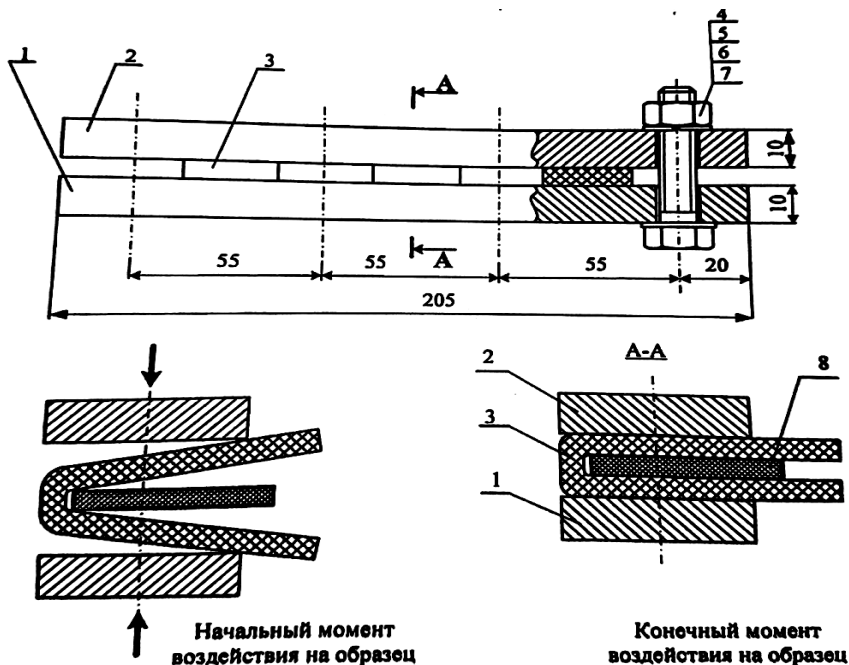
Приспособление для деформирования образца: 1 – нижний зажим; 2 – верхний зажим; 3 – образец материала; 4 – болт М8; 5 – шайба пружинная М8; 6 – шайба М8; 7 – шайба М8; 8 – контрольная полоска
